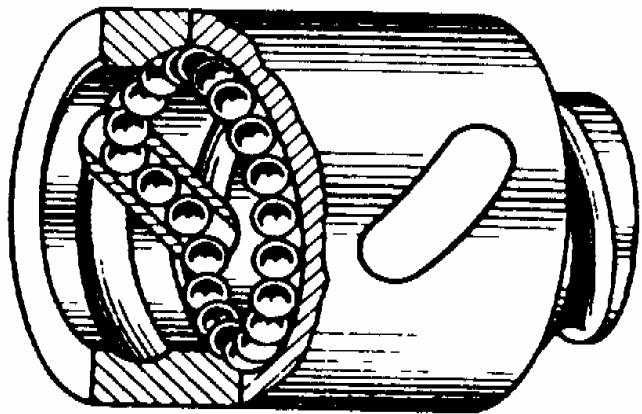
Наружная обойма шариковинтовой передачи
